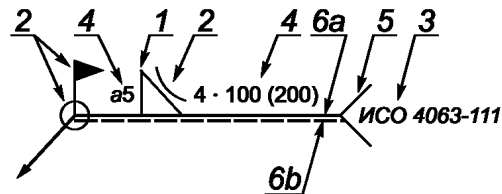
Пример графического обозначения для требуемого уровня качества сварки
